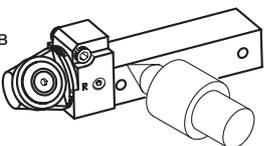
Руководство по эксплуатации фрезеровальных накаток 290222
